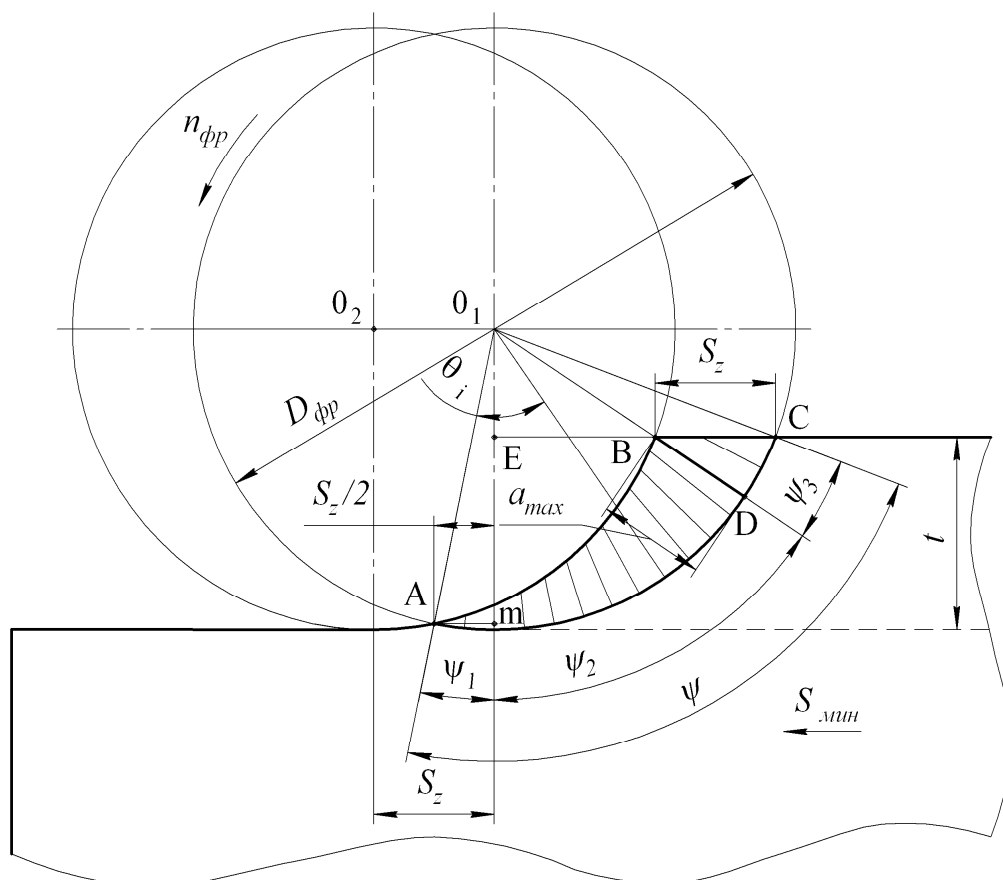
Схема сечения среза одним зубом фрезы при цилиндрическом фрезеровании (встречном)
